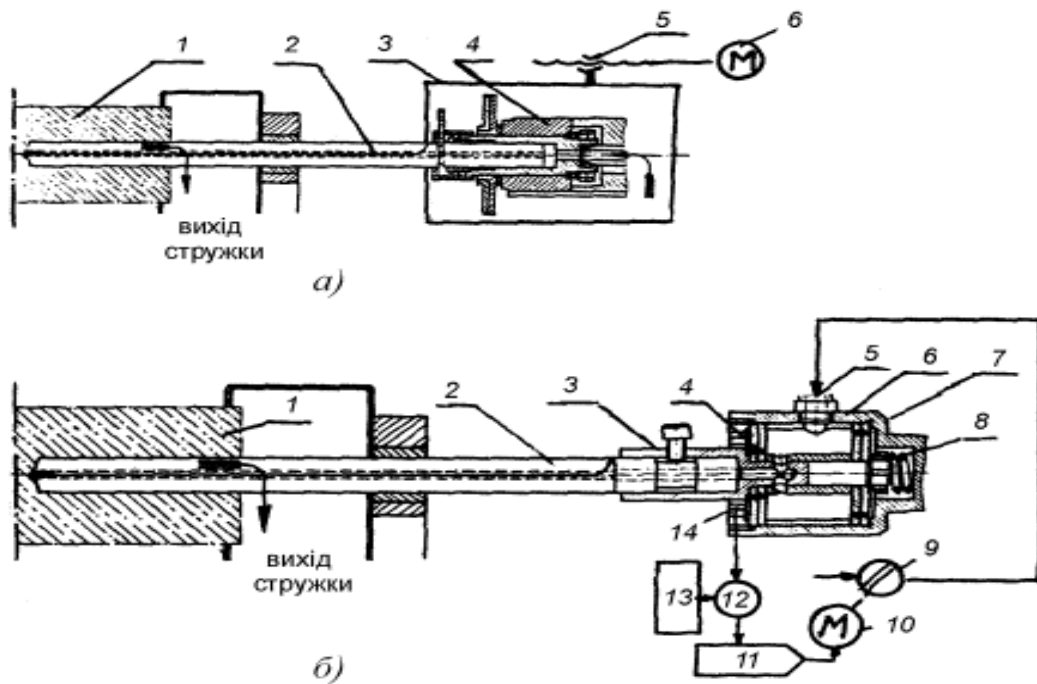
Схеми приводу для глибокого свердління гарматними свердлами:
